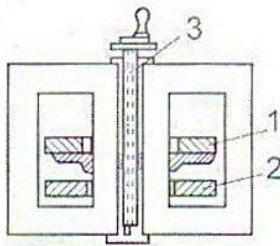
Схематичний вигляд зварювального трансформатора типу ТЗ: 1 – первинна обмотка; 2 – вторинна обмотка; 3 – гвинт з гайкою
